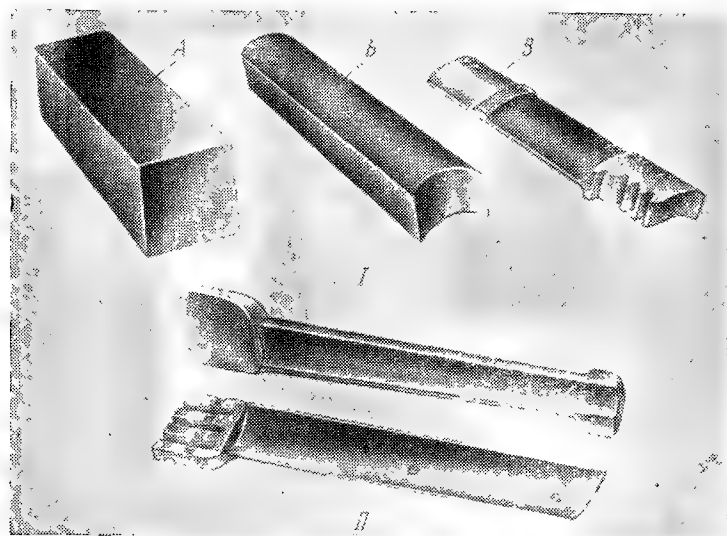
Типовые конструкции рабочих лопаток по видам рекомендуемых заготовок:
